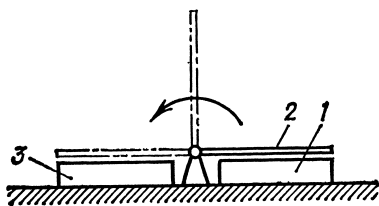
Схема устройства для сборки и сварки ферм
